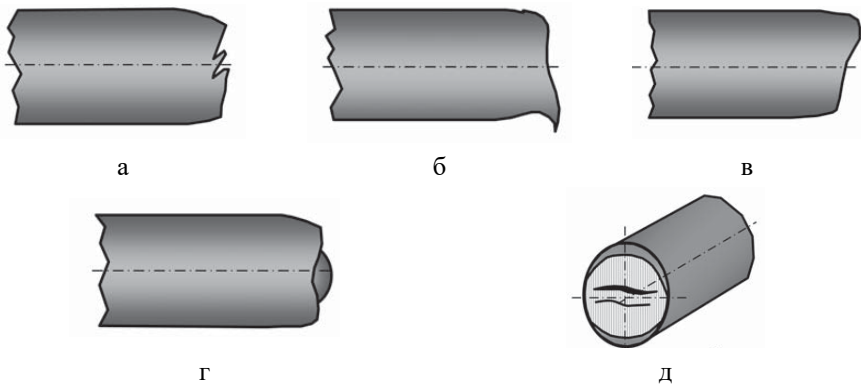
Дефекти під час різання вихідних заготовок: а – виривки; б – задир з утяжкою; в – збільшений скіс торця; г – вириви, грубий зріз; д – торцеві тріщини, паралельні робочим крайкам ножів)
